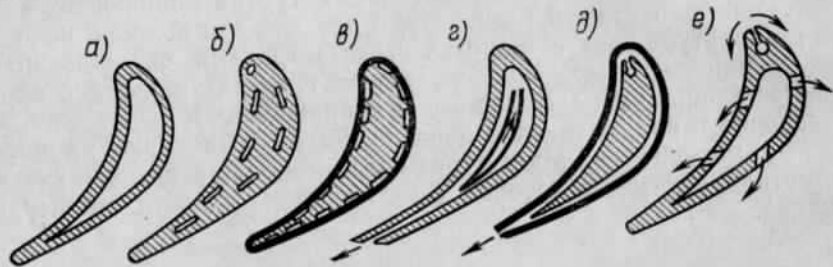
Способы воздушного охлаждения сопловых и рабочих лопаток
